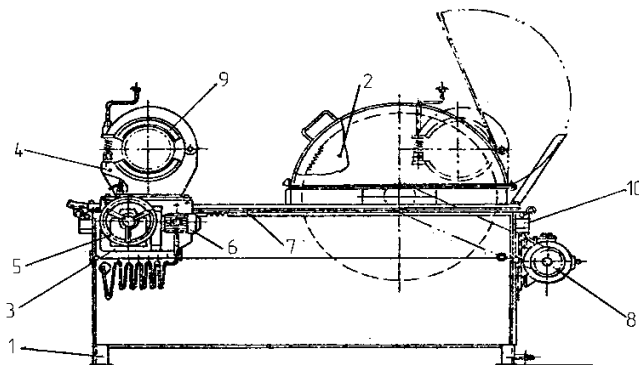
Станок для резки пластмассовых труб: 1 - станина; 2 - дисковая пила; 3 - суппорт станка; 4 - зажим для труб; 5 - штурвал; 6 - электродвигатель суппорта; 7 - зубчатая рейка; 8 - электродвигатель пилы; 9 - вкладыш; 10 - конечный выключатель
